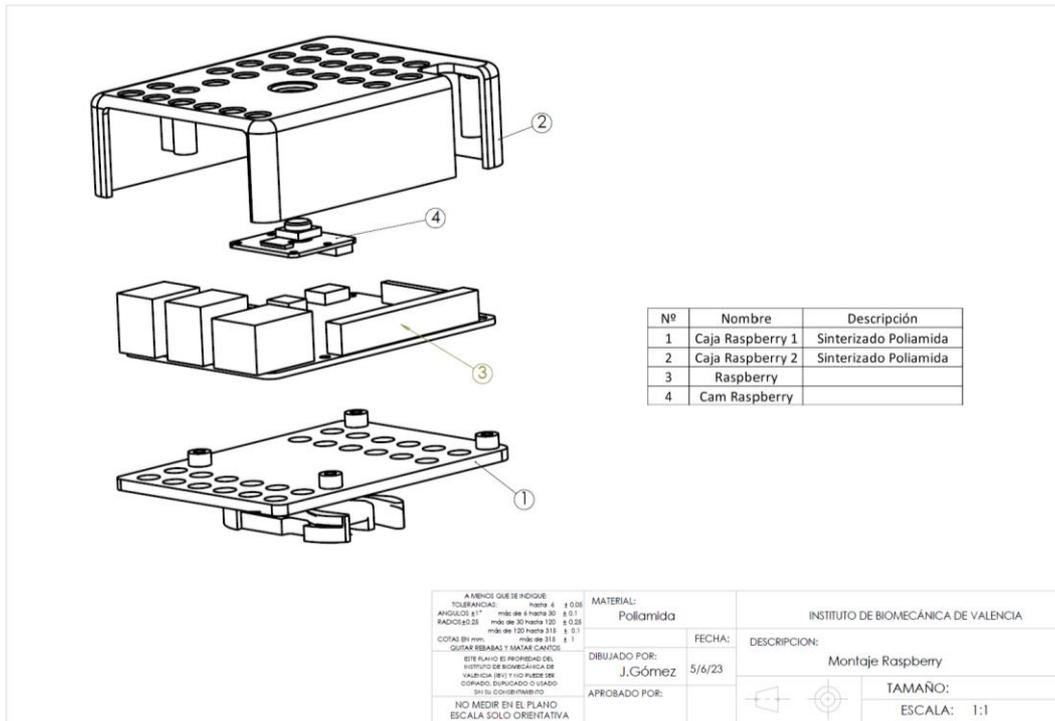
Planos de detalle de los componentes de la caja soporte de las cámaras.
